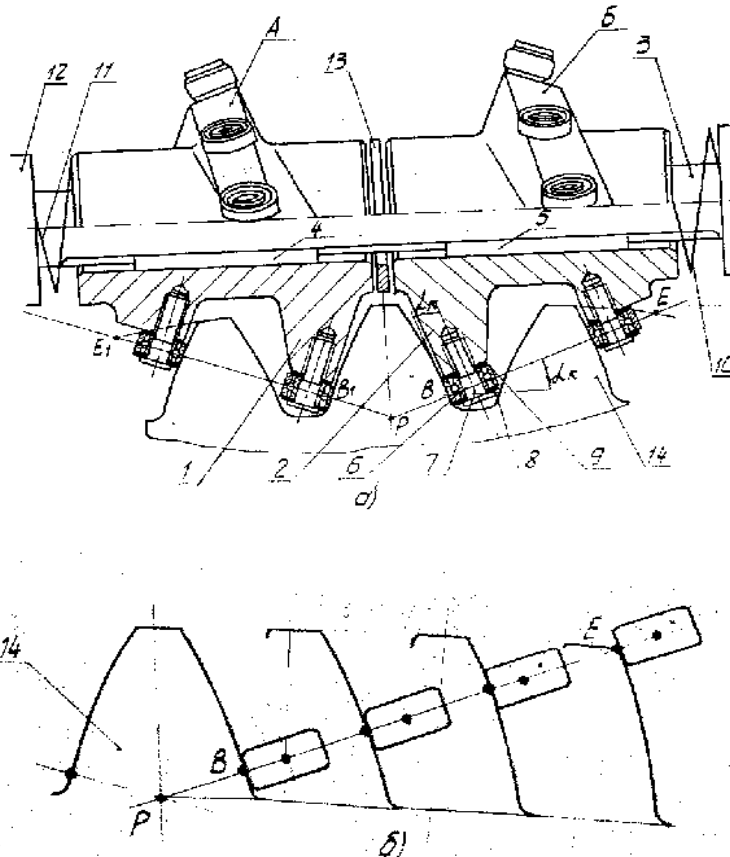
Червячный накатник для отделочно-упрочняющей обработки зубчатых колес ППД: а – общий вид инструмента; б – схема взаимодействия накатного элемента с боковой поверхностью зуба колеса
